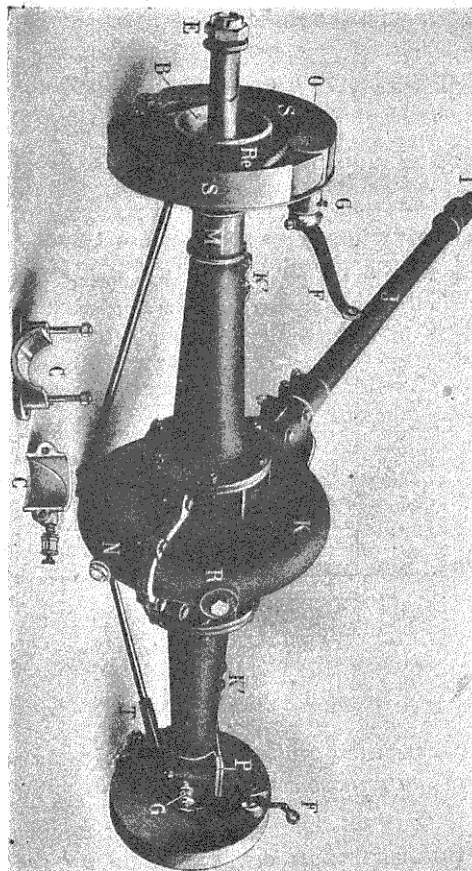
Vue d'un pont arrière oculi. m. type D-lace.
